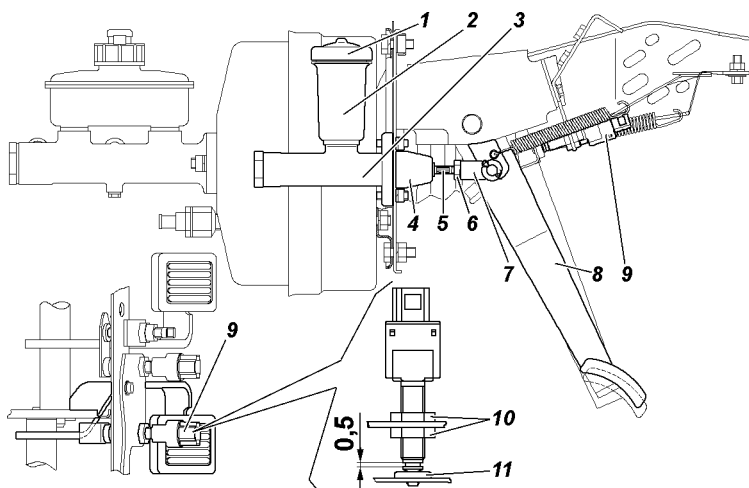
Привод главного цилиндра выключения сцепления:
